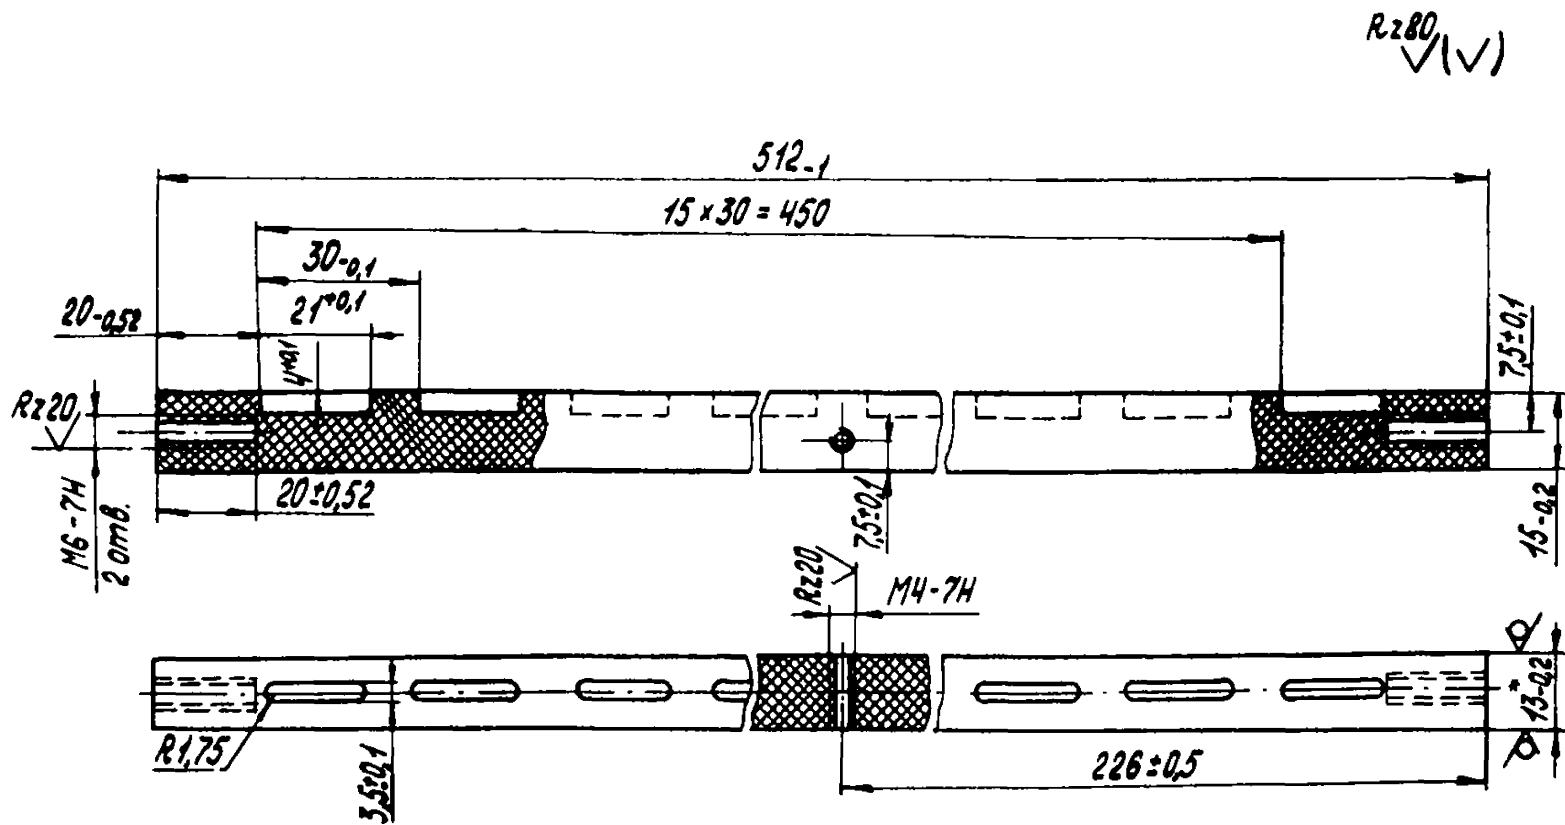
Планка кассеты для установки контрольных образцов через байпас.
